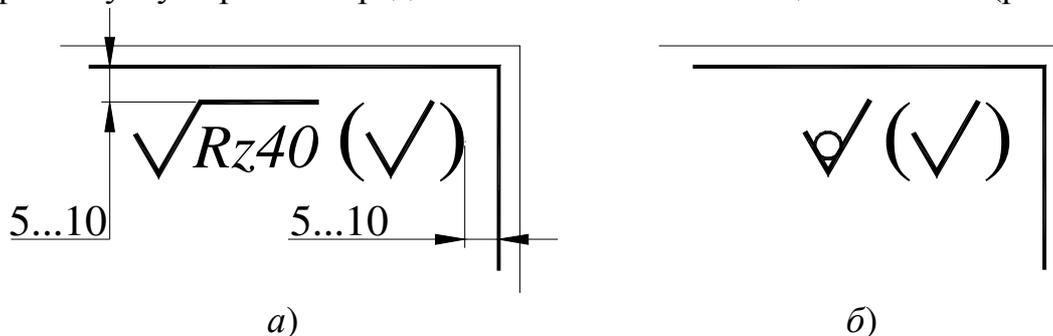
Обозначение одинаковой шероховатости (а) или шероховатости поверхностей, не обрабатываемых по данному чертежу (б)
